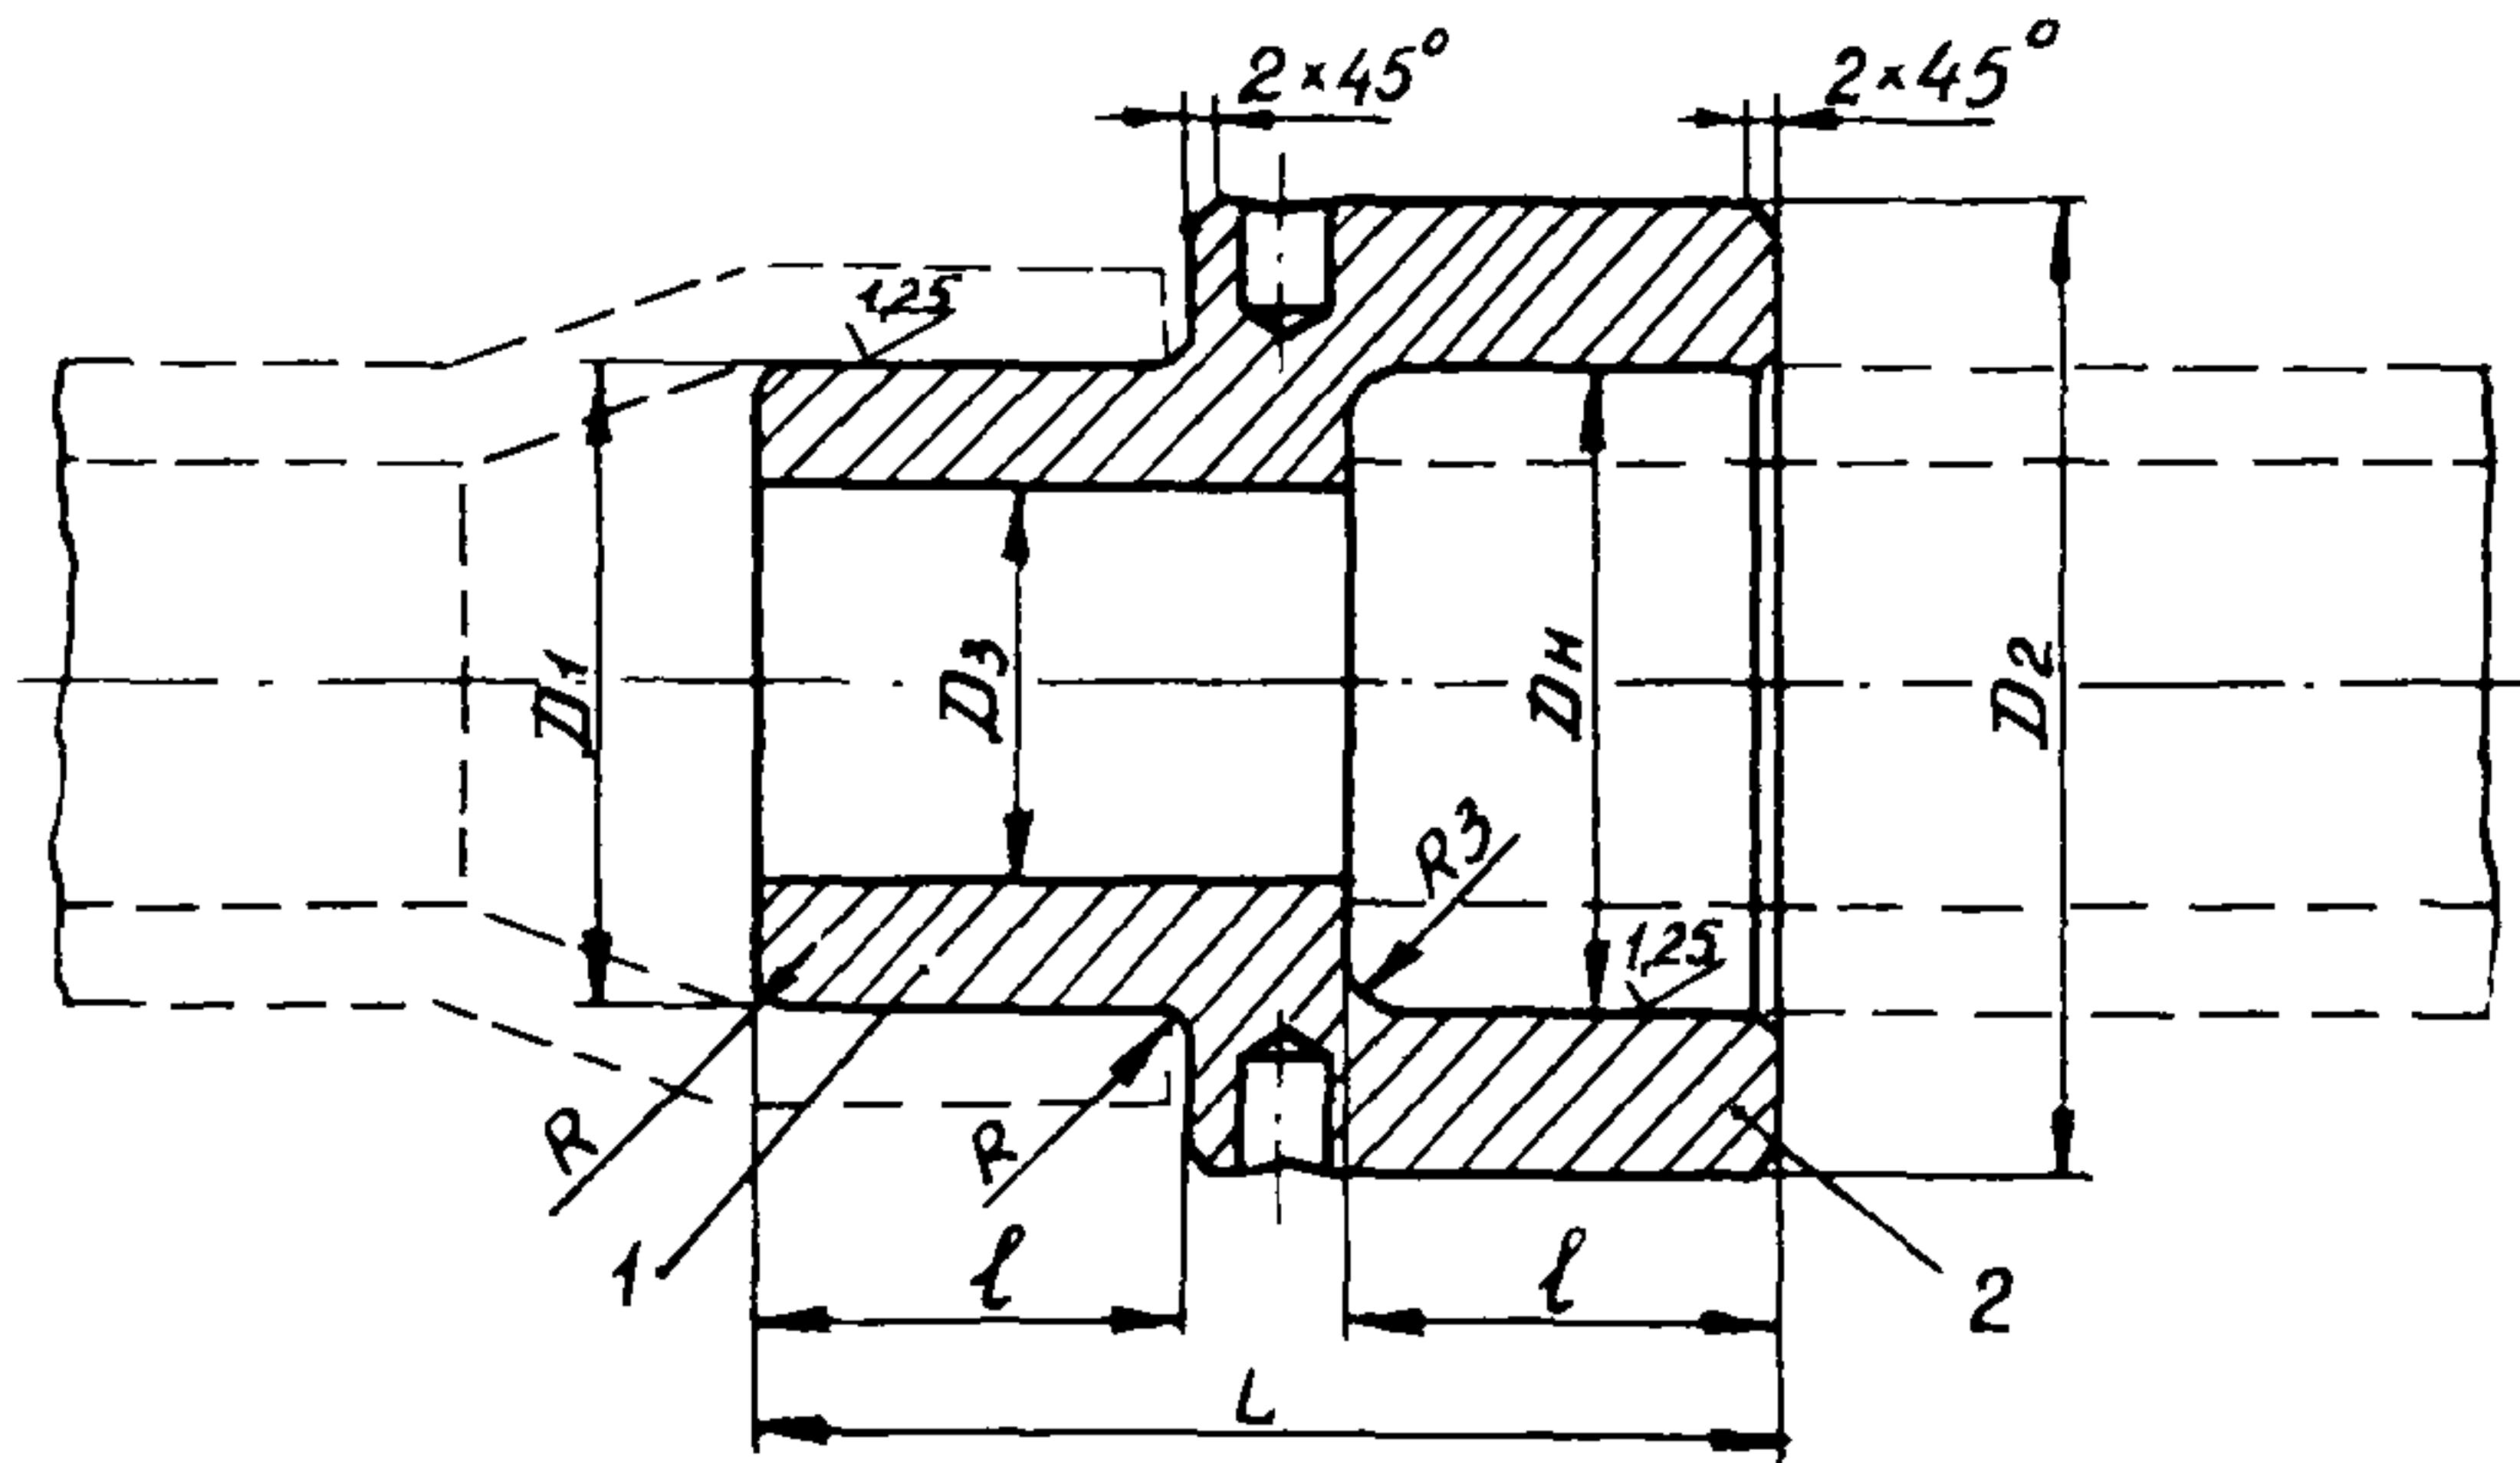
Схема нагревательного инструмента газопламенного нагрева для сварки полиэтиленовых труб враструб:
